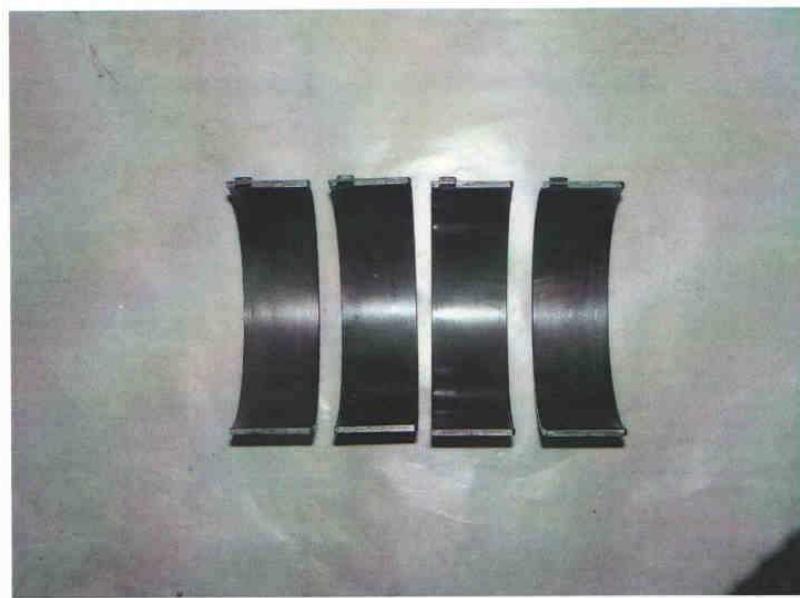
Вкладыш шатунного подшипника (двигатель, заправленный штатным маслом)
